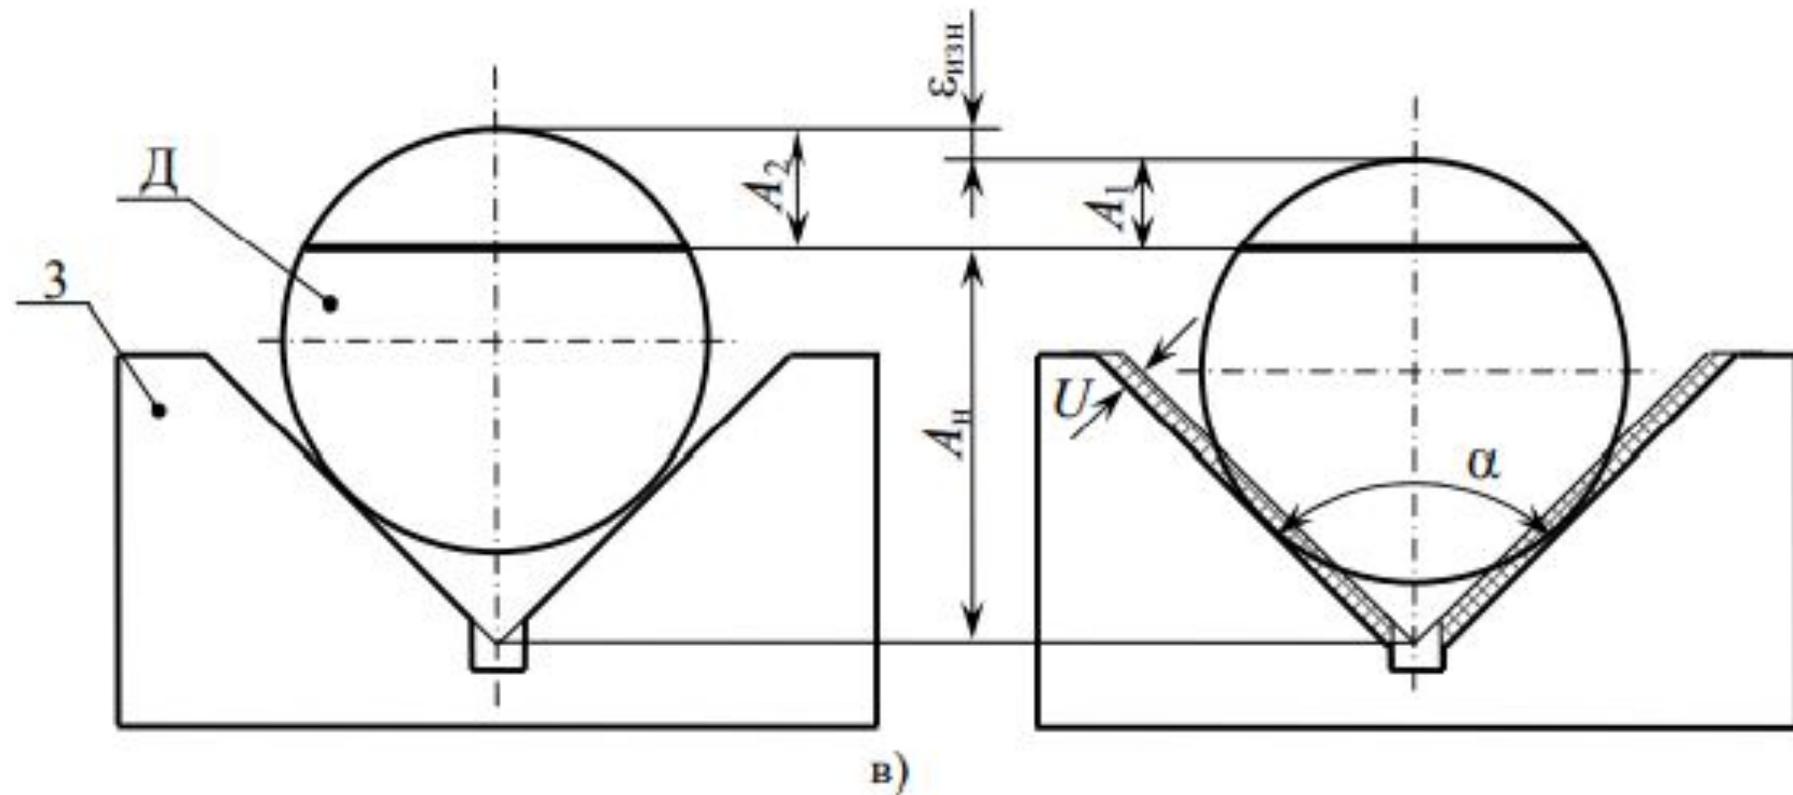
Формирование погрешности износа при различных способах установки заготовки в приспособлениях:
